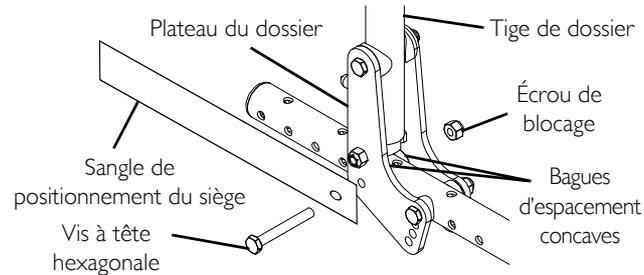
Installation/Remplacement des sangles de positionnement du siège
